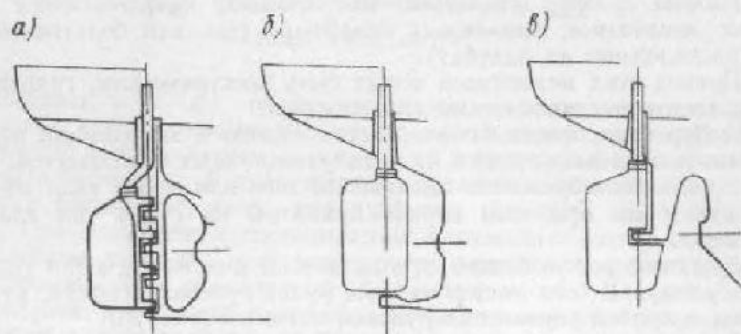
Типы рулей: а — обыкновенный; б — балансирующий; в — полубалансирующий одновинтового судна.
